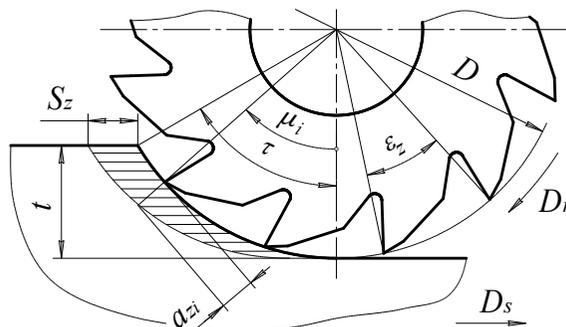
Схема процесса резания при цилиндрическом фрезеровании
